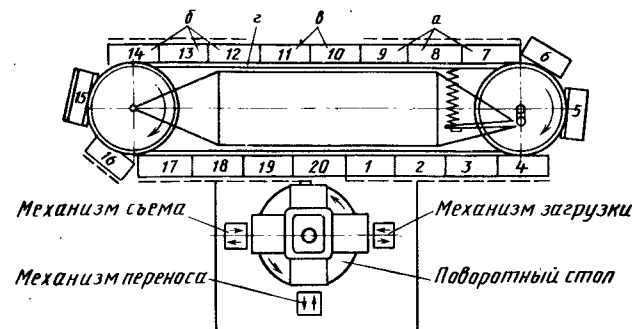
Схема обработки хвостовика рабочей лопатки компрессора на горизонтально-протяжном автомате непрерывного действия: а, б — рабочие ползушки с протяжками; в — холостые ползушки; г — транспортер
